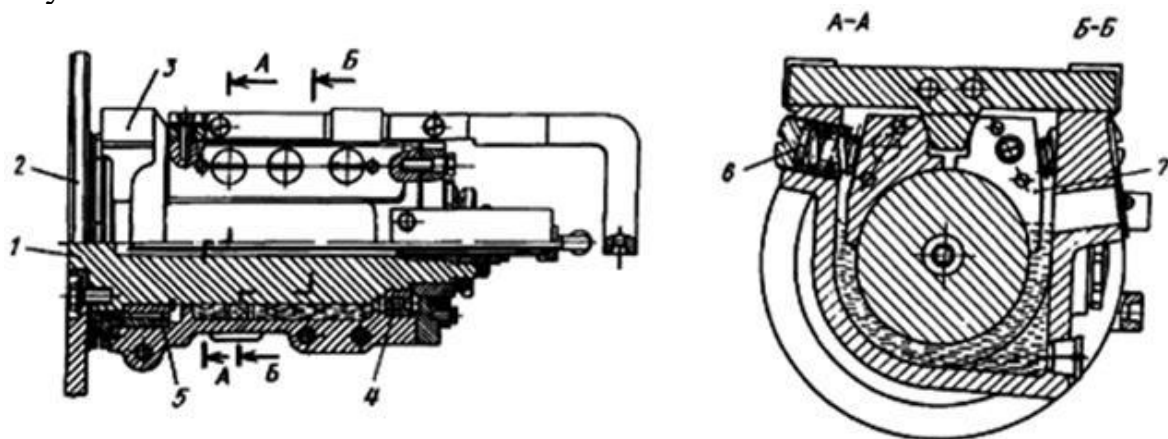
Скользящий токоподвод машины шовной сварки
